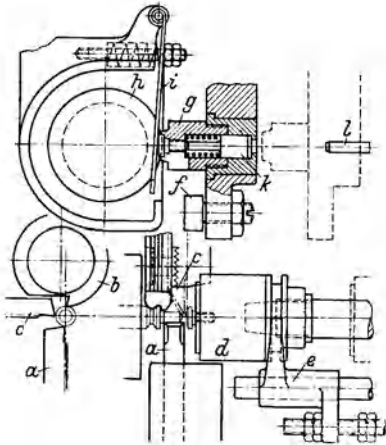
Bearbeitung einer Kopfschraube mit Schlitz im doppelten Arbeitsverfahren.
